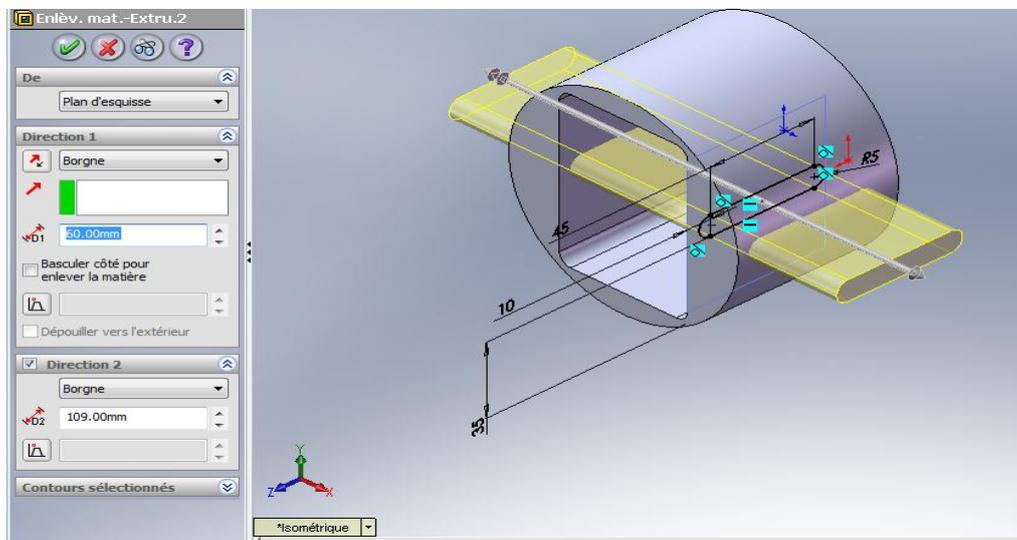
40. Enlèvement de matière sur le cylindre (plan Droite).
